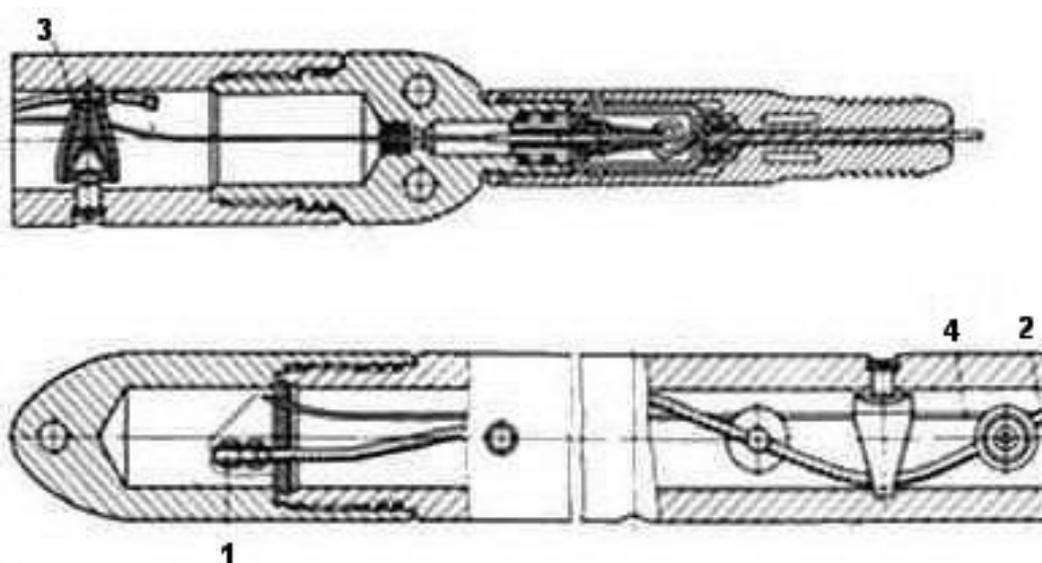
Устройство корпусного кумулятивного перфоратора ПК-105ДУ: 1) - взрывной патрон; 2) - детонирующий шнур; 3) - кумулятивный заряд; 4) – электропровод
